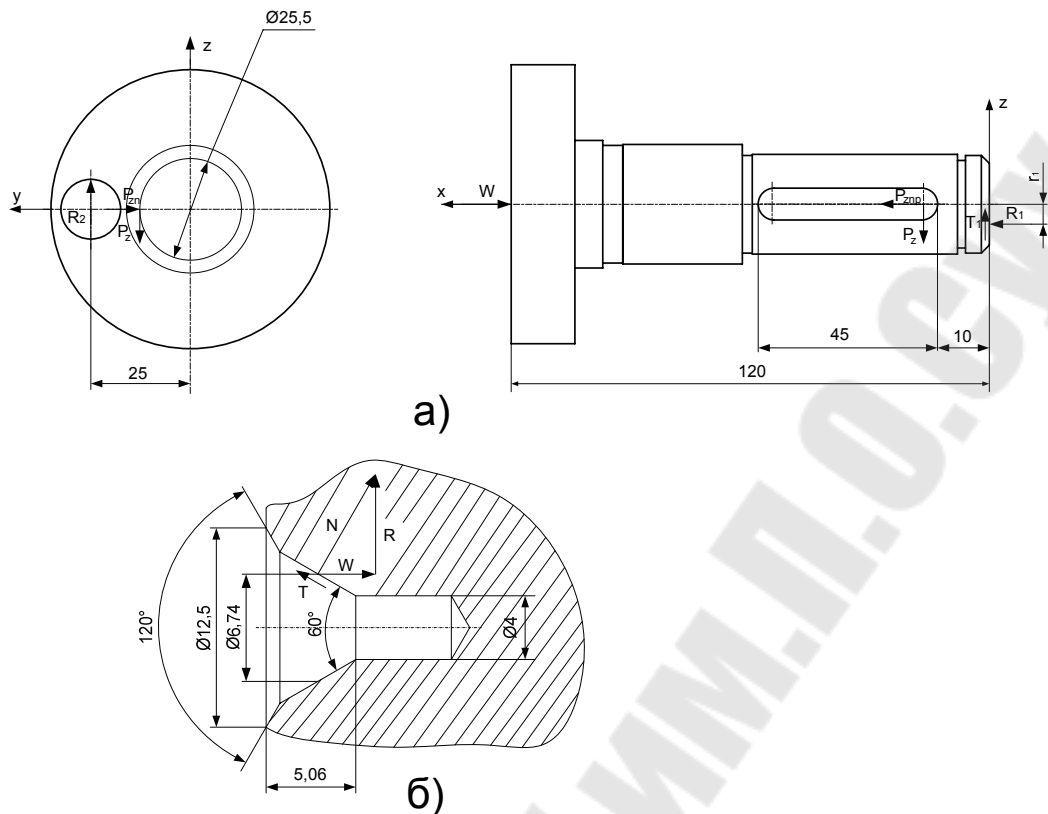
Схема действия сил на заготовку при фрезеровании шпоночного паза.
